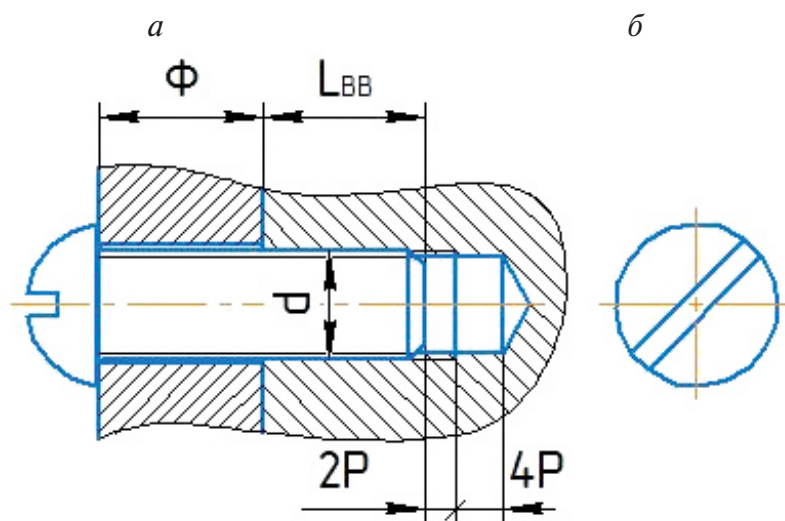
Конструктивное изображение соединения деталей винтом с цилиндрической головкой:
